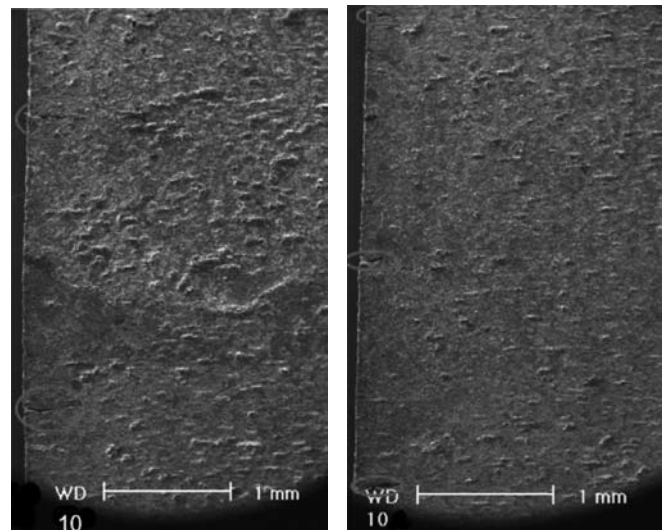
Grietas en una probeta con soldadura ensayada a creep (265 MPa durante 300 h).
